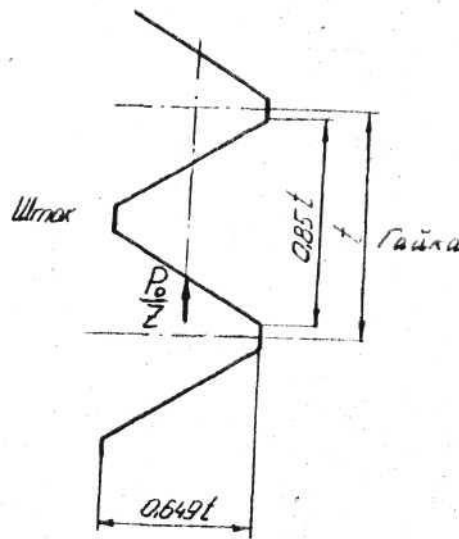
Розрахункова схема різьби штока на згин
